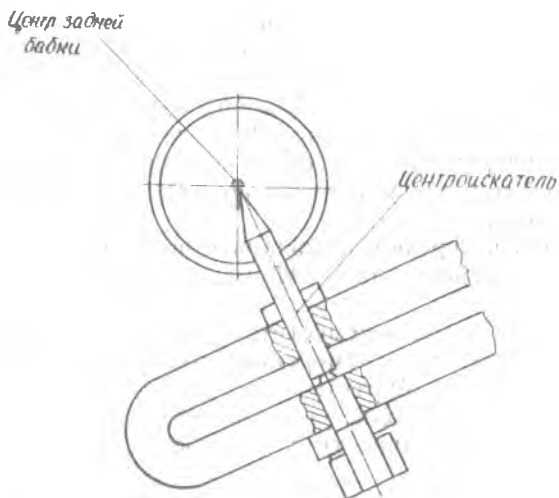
Схема определения оси заготовки с помощью центроискателя
